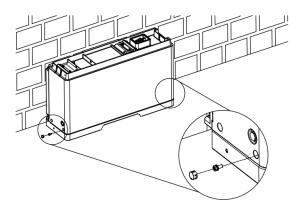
Befestigen Sie das installierte Batteriemodul
